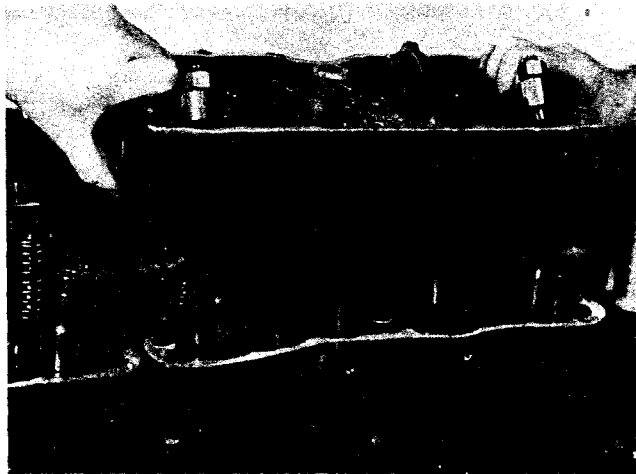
, (N100147). Remoción del conjunto de caja de balancines.
